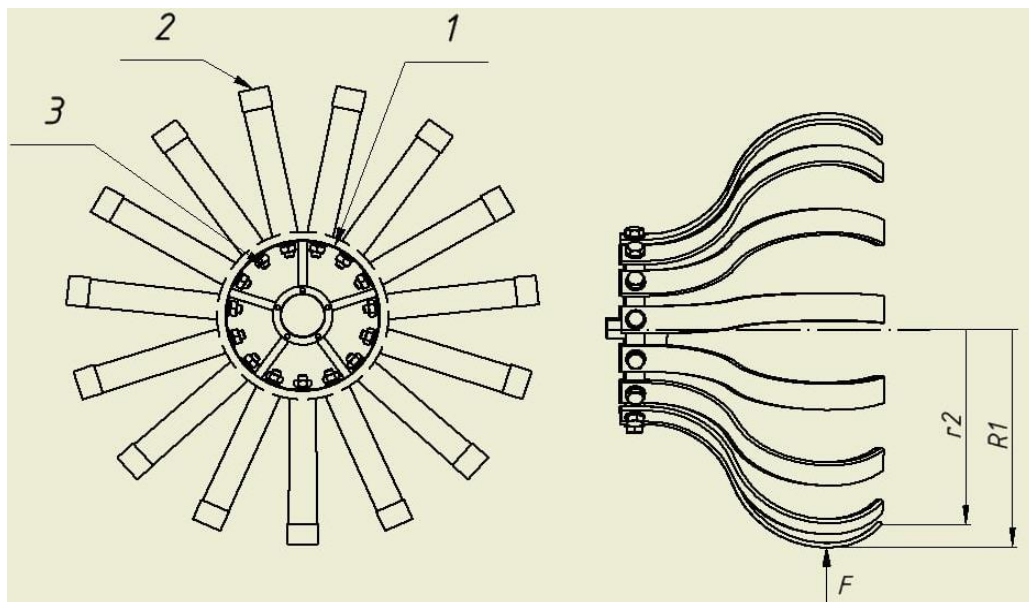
Схема колеса з пружними елементами типу «спиця»
